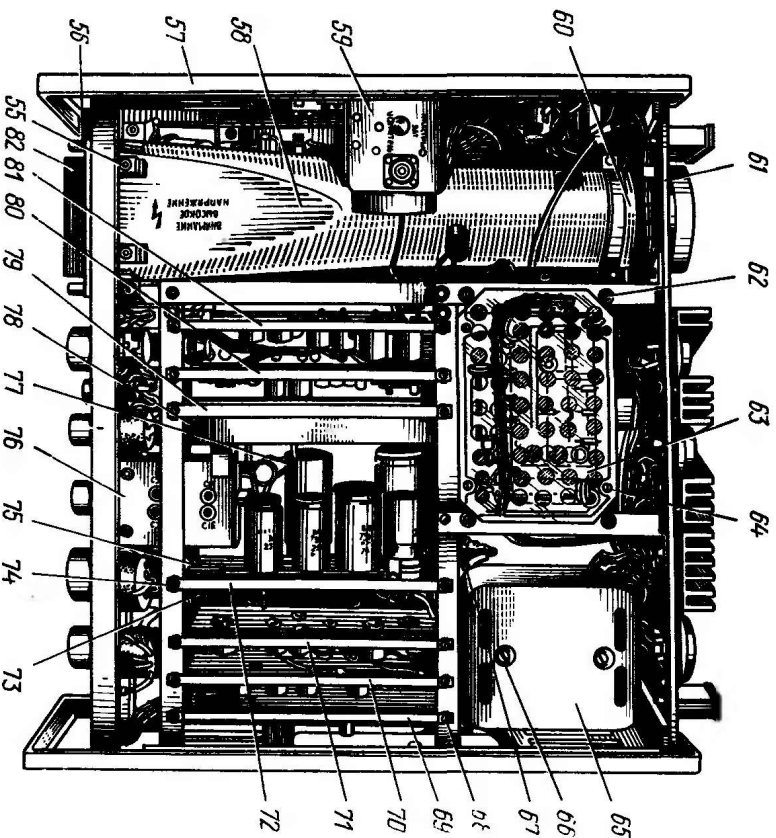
Вид на индикатор со снятой верхней крышкой:
